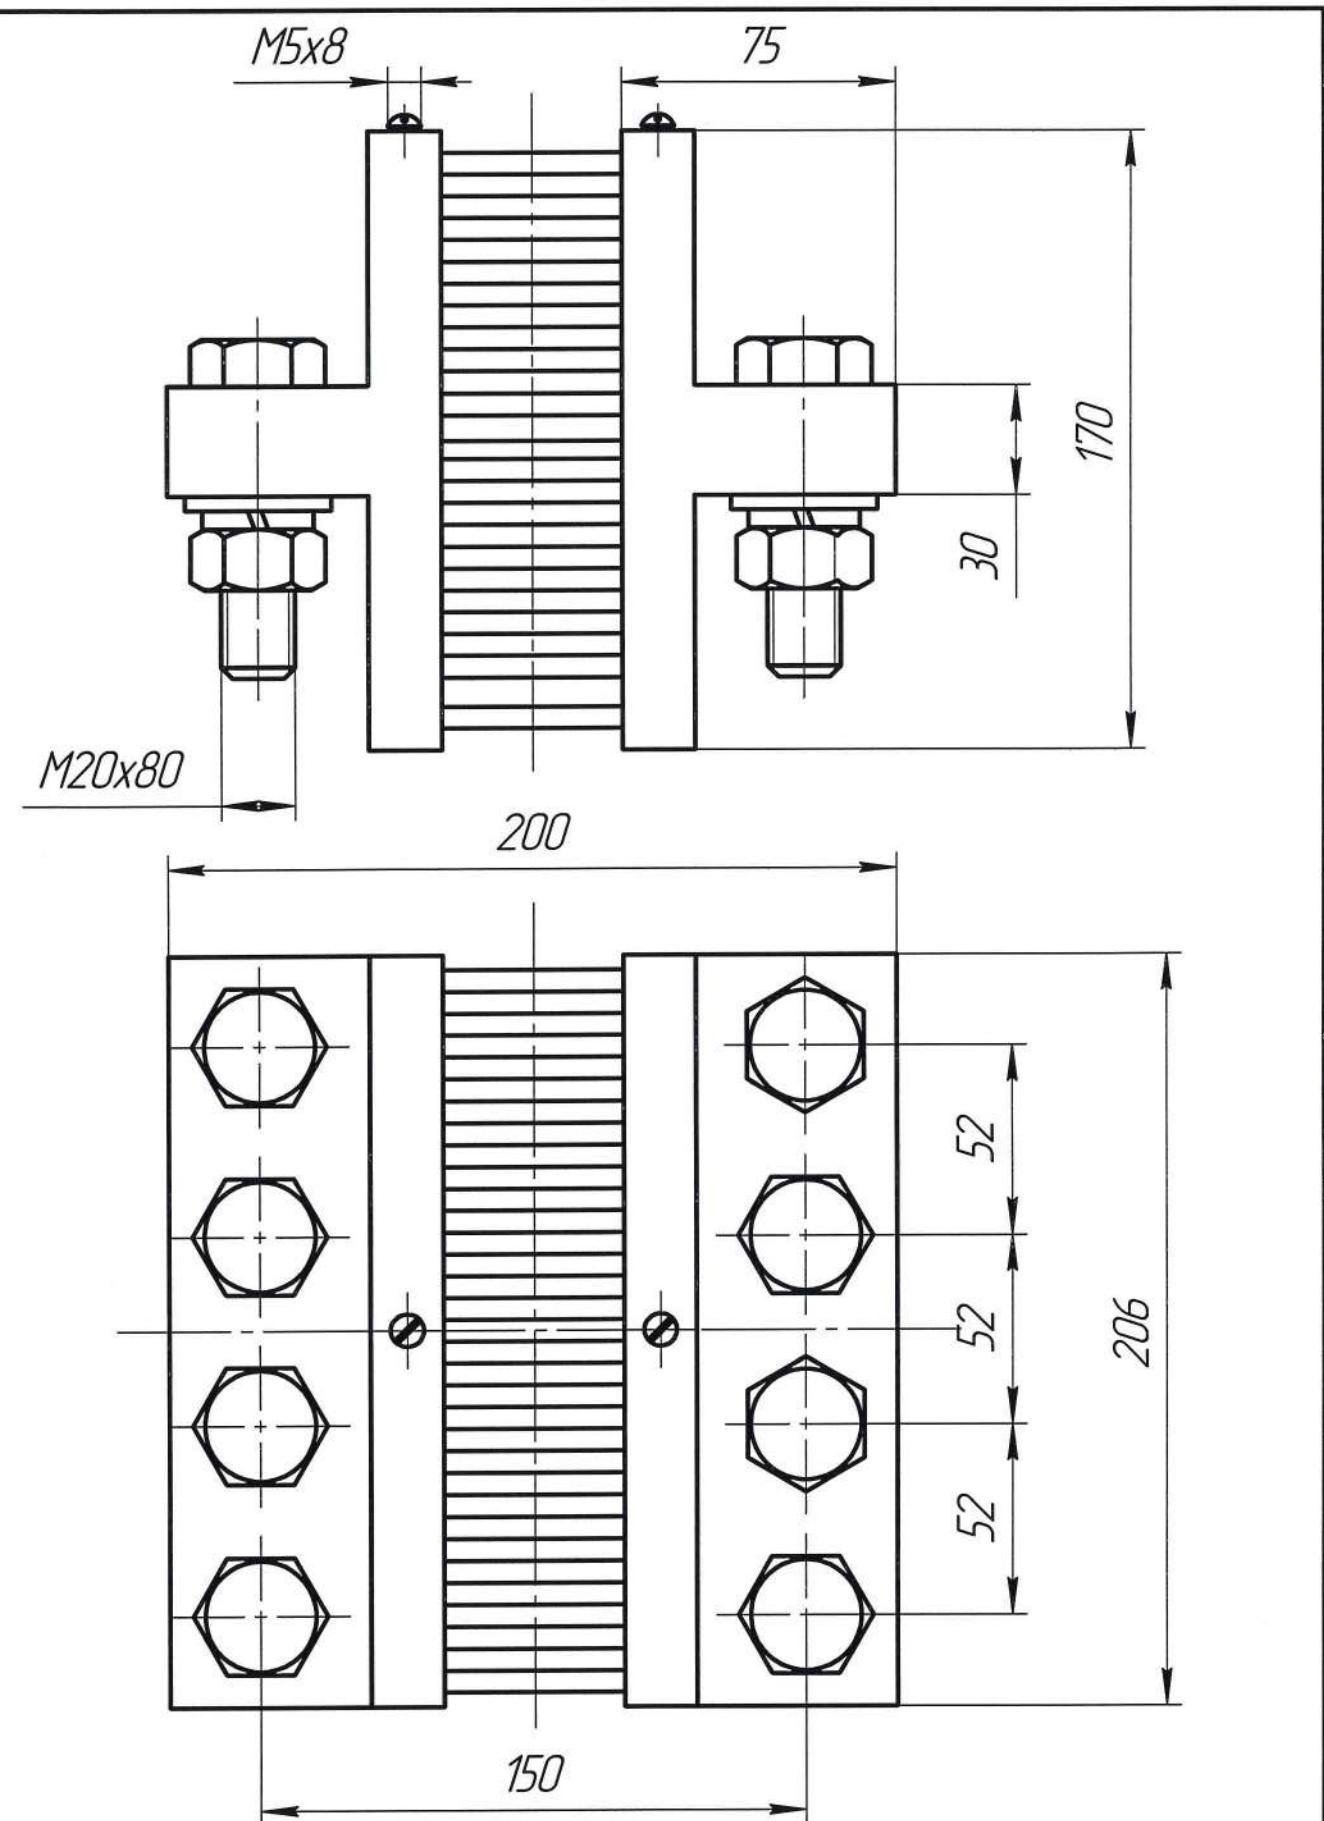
Габаритные размеры шунта 75 ШИС на ток 10000 А.
